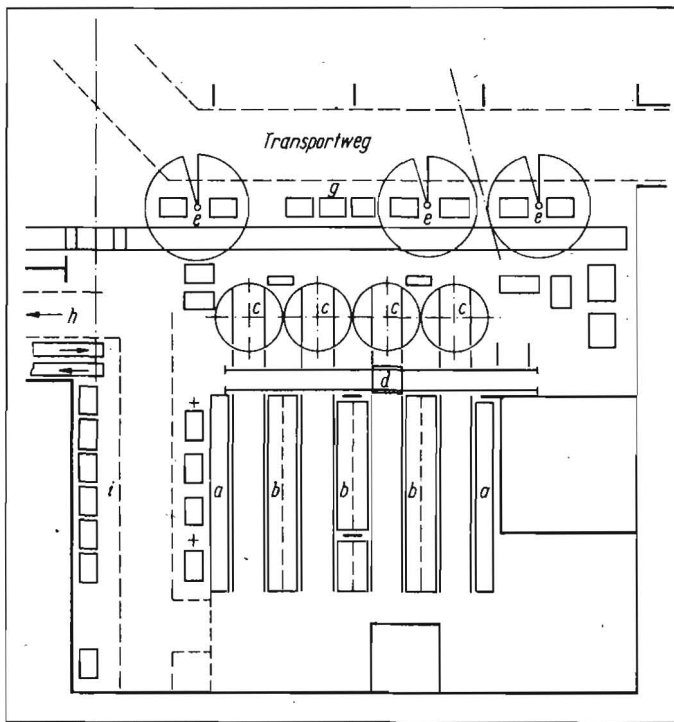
Prinzipskizze für den Aufbau einer Schadaufnahme:
